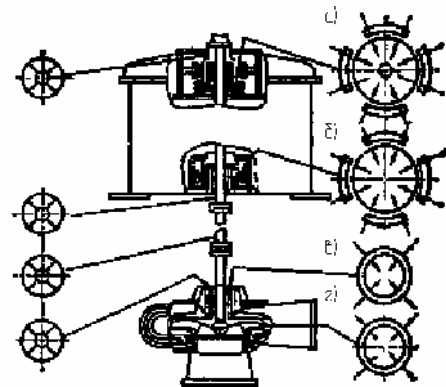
Места проверки биения вала индикаторами и проверяемых зазоров:
